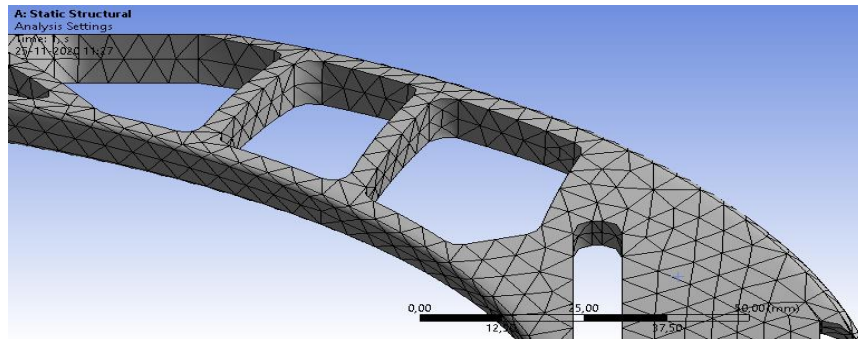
Vista 2 rediseño N°3 de eslabón pierna izquierda.
